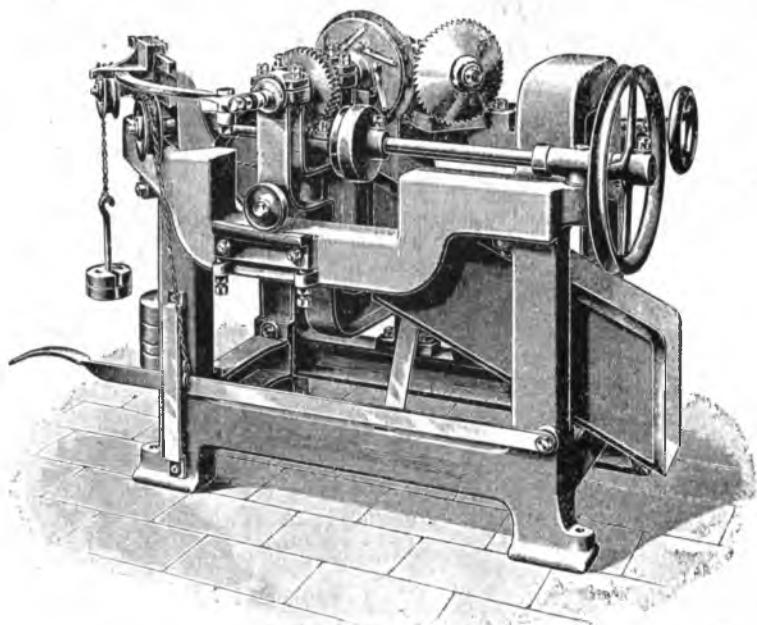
Станок для округления днищ и скашивания краев с двумя ножами.
